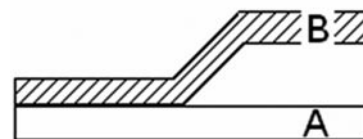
Схема проведения сварки взрывом: А – опорная плита, В – метаемая пластина
